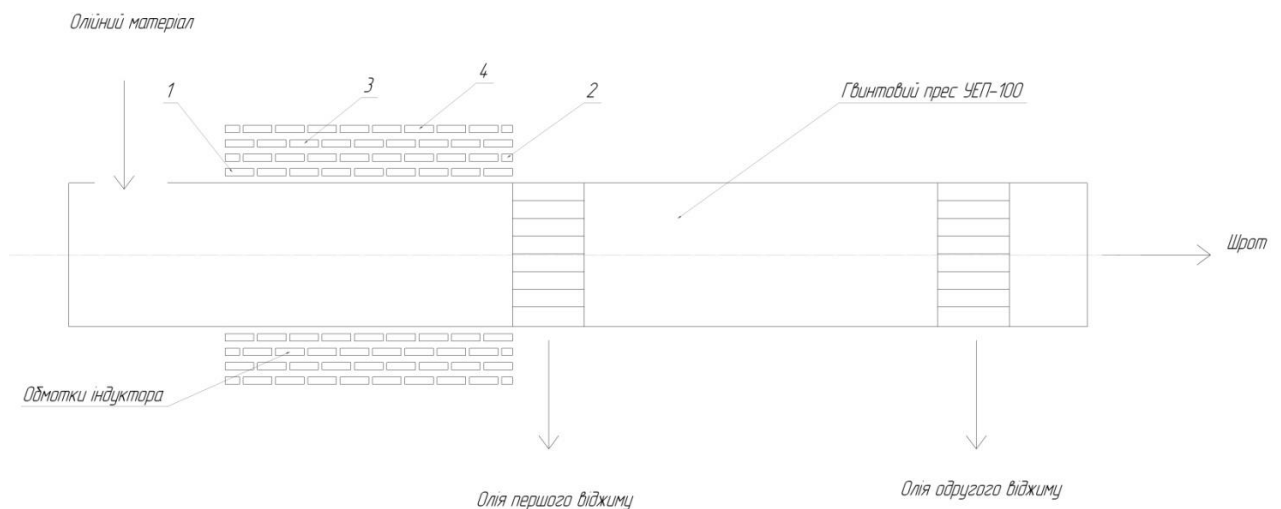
Встановлення індукційного нагрівача на корпус прес-екструдера УЕП-100:
